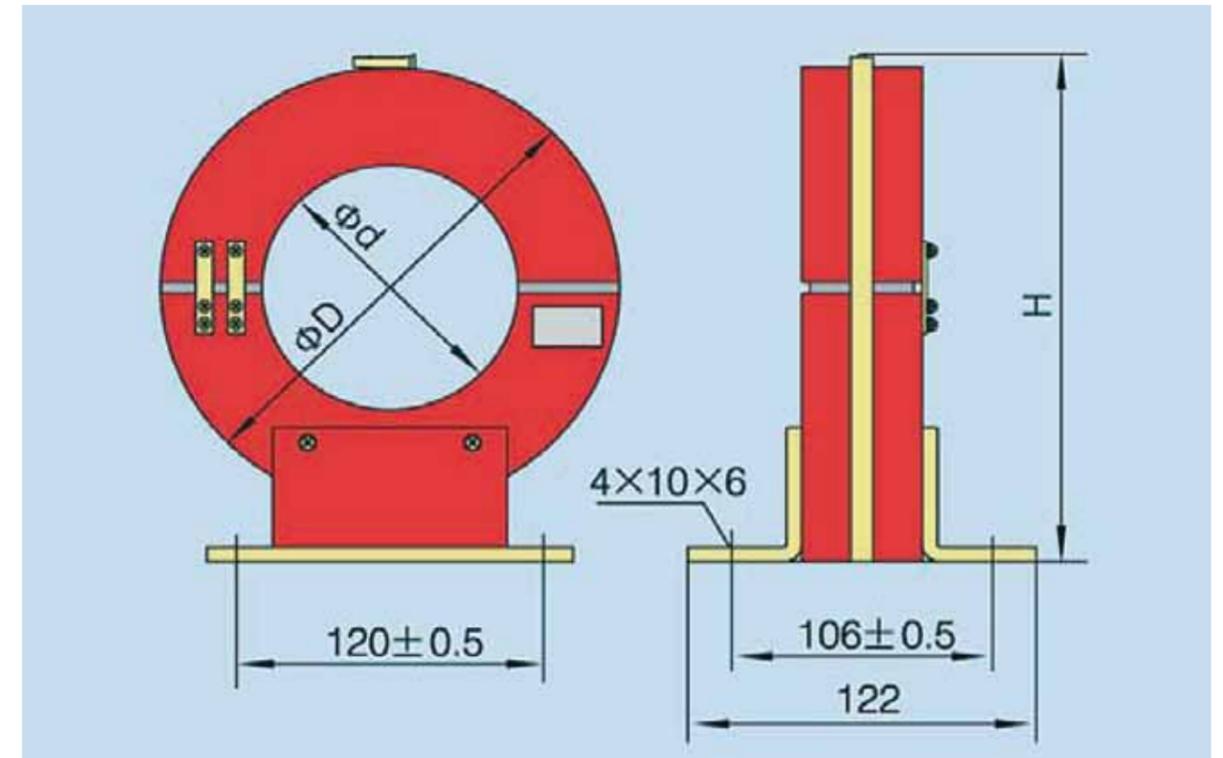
Внешний вид и размеры трансформатор тока нулевой последовательности L XK-80(100,120)
